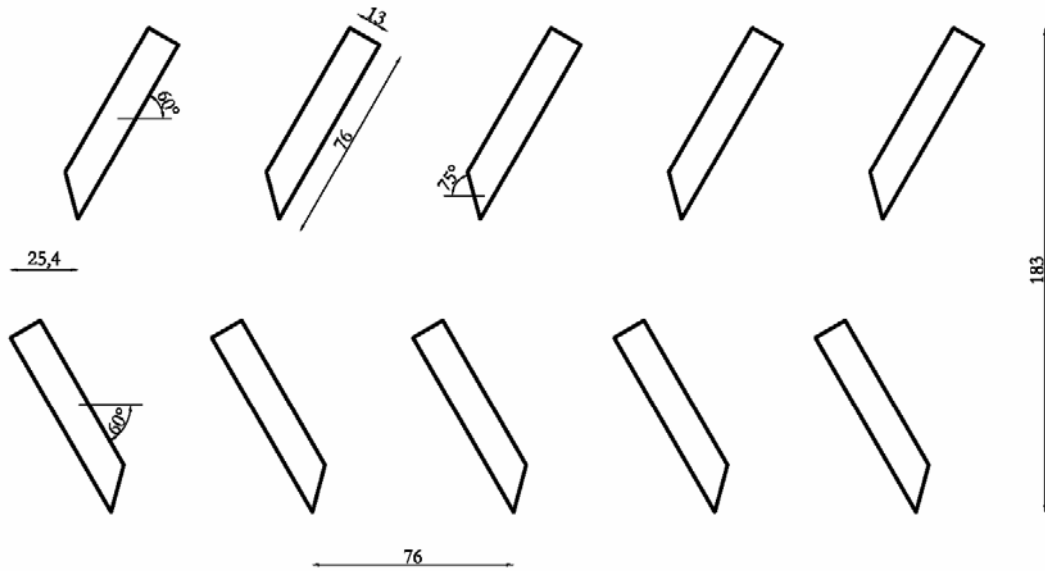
Dimensiones principales del separador de gotas "Wooden-lath".
